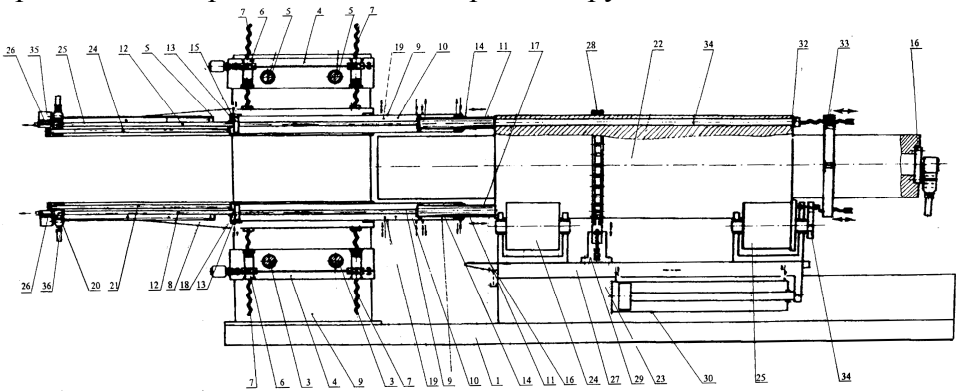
Кінематична схема верстату «Дуга-13»
